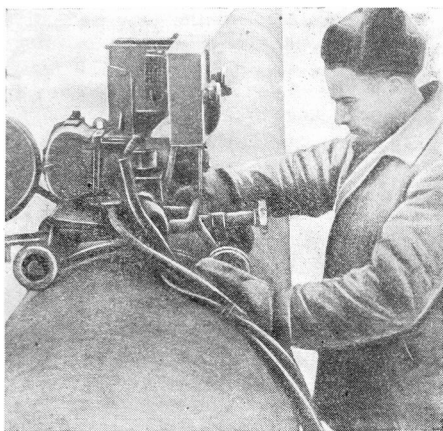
Общий вид сварочного автомата под слоем флюса.
